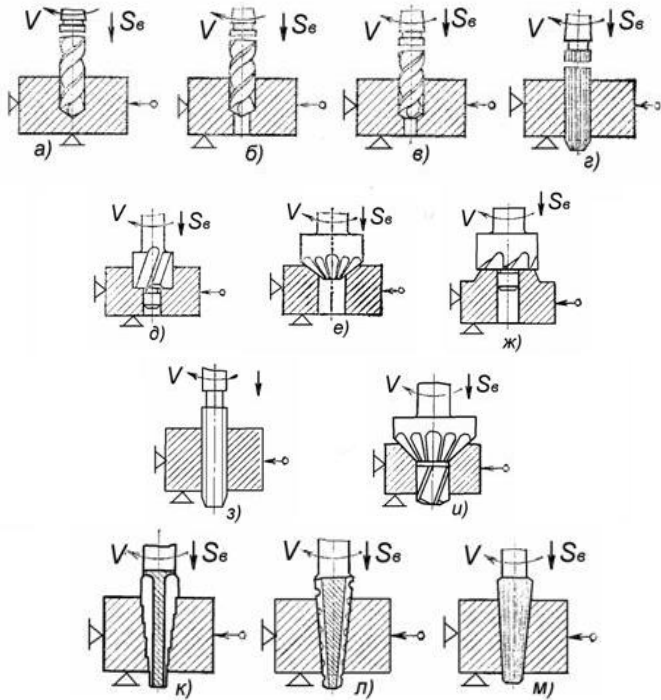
Інструменти та їхні рухи при обробці отворів на свердлувальних верстатах
